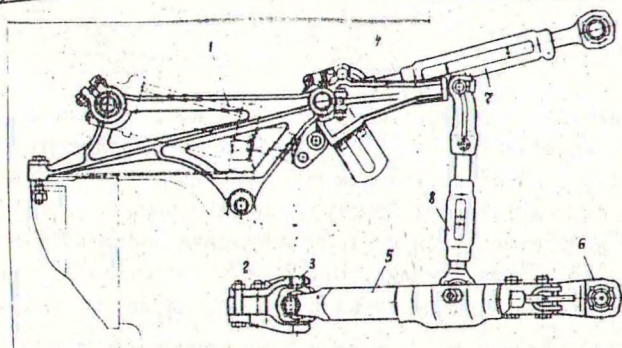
Механизм задней навески: 1 - кронштейн; 2- скоба; 3 - шаровой шарнир; 4 - подъемный рычаг; 5 - нижняя тяга; 6 - выдвигаемая обойма; 7 - тяга верхняя; 8 - раскос.
